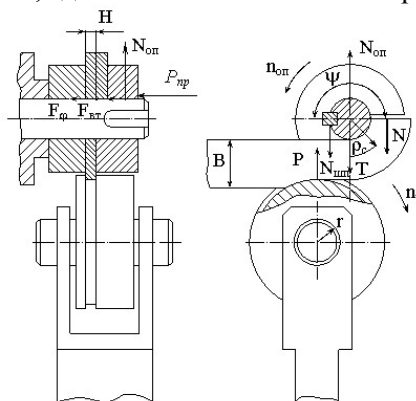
Розрахункова схема процесу неперервного формоутворення навивних заготовок
